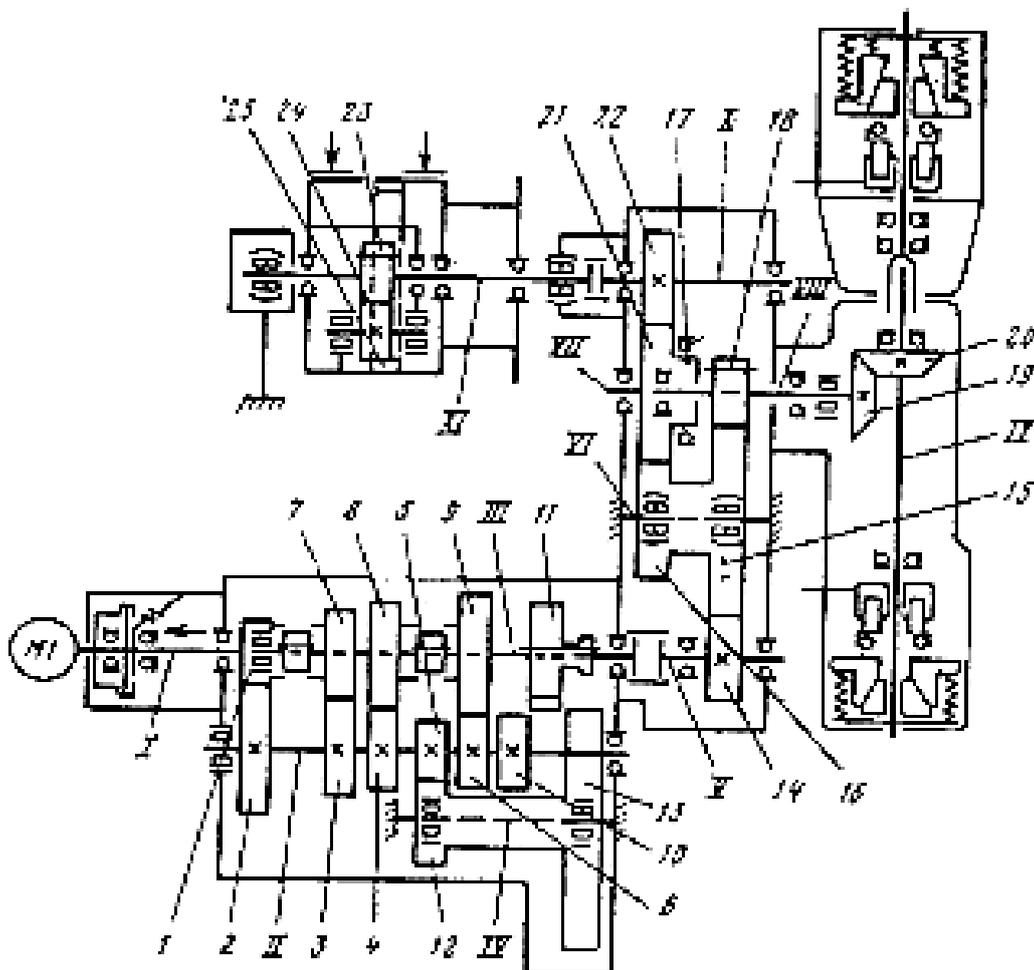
Кинематическая схема станка СКБ-4: 1–25 – шестерни с числом зубьев: 20, 43, 38, 31, 20, 22, 26, 33, 42, 15, 45, 22, 60, 28, 54, 36, 26, 29, 26, 44, 30, 41, 24, 78; I – первичный вал коробки передач; III – вторичный вал коробки передач; IV – вал левого вращения; V – первичный вал раздаточной коробки; VI – ось промежуточных шестерен; VII – вторичный вал раздаточной коробки
